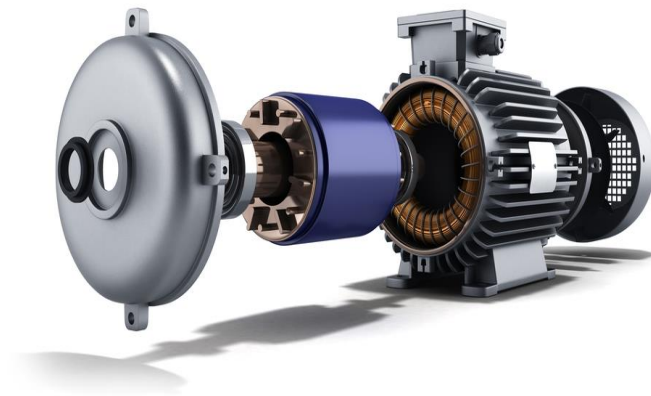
vue du moteur asynchrone à cage d'écureuil
